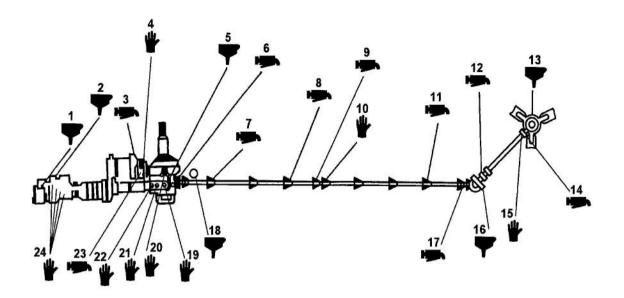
Смазка агрегатов двигателей и трансмиссии
